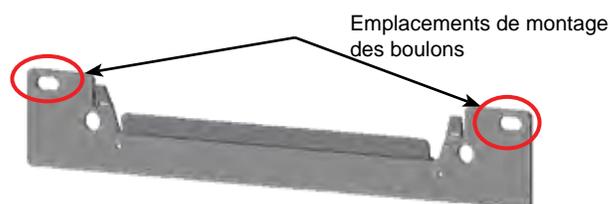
Ajout de butée en caoutchouc pour fixation au mur
